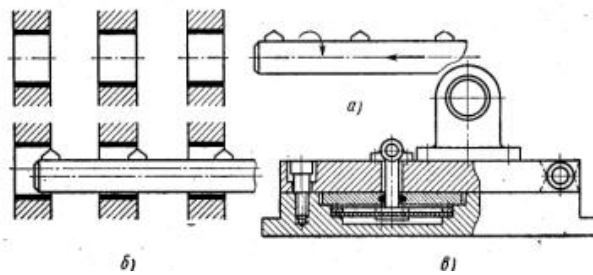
Схема розточувального кондуктора з підймальним пристроєм
